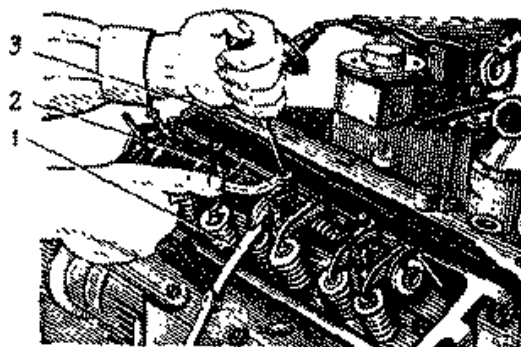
Регулировка зазора между коромыслом и клапаном:
